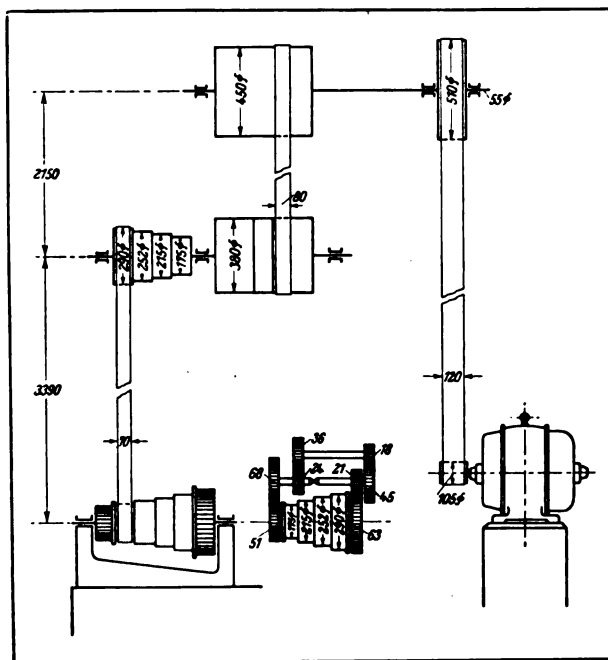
Getriebeplan einer Stufenscheibendrehbank.
